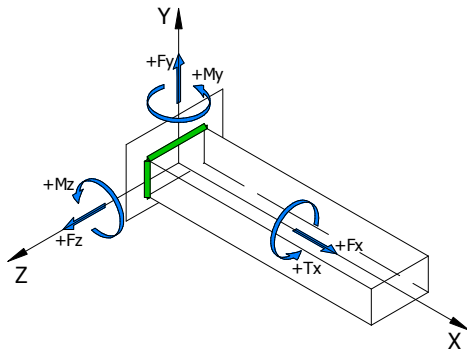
Koordinatensystem für die Schweißnahtberechnung
